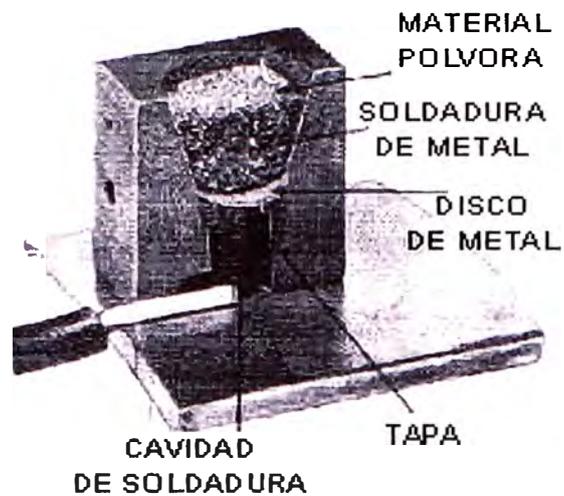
Conexión Soldada entre dos cables y superficie
